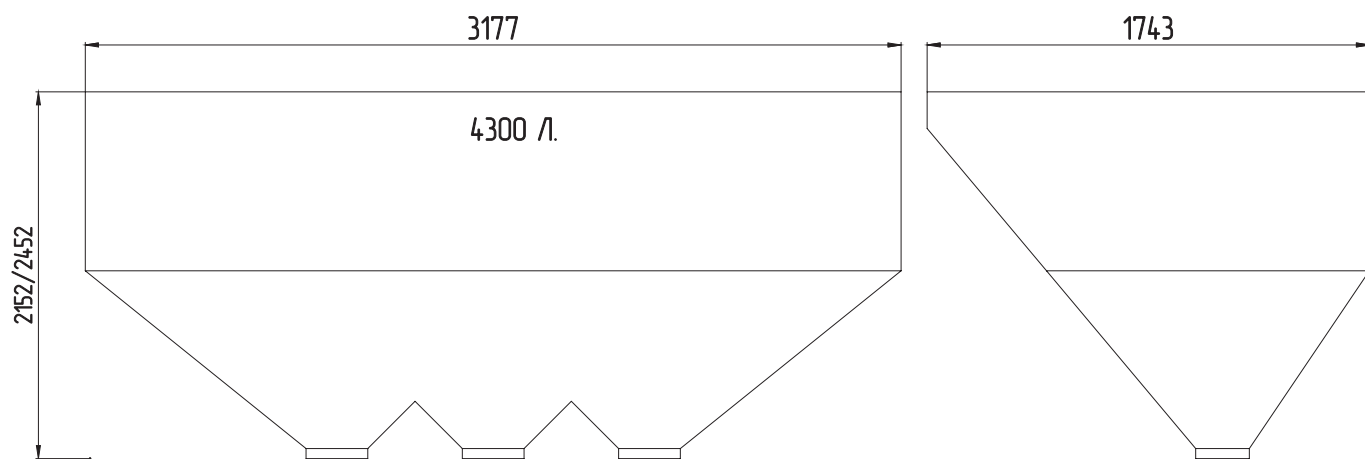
Габаритные размеры топливного бункера 4300 л 3 горла
